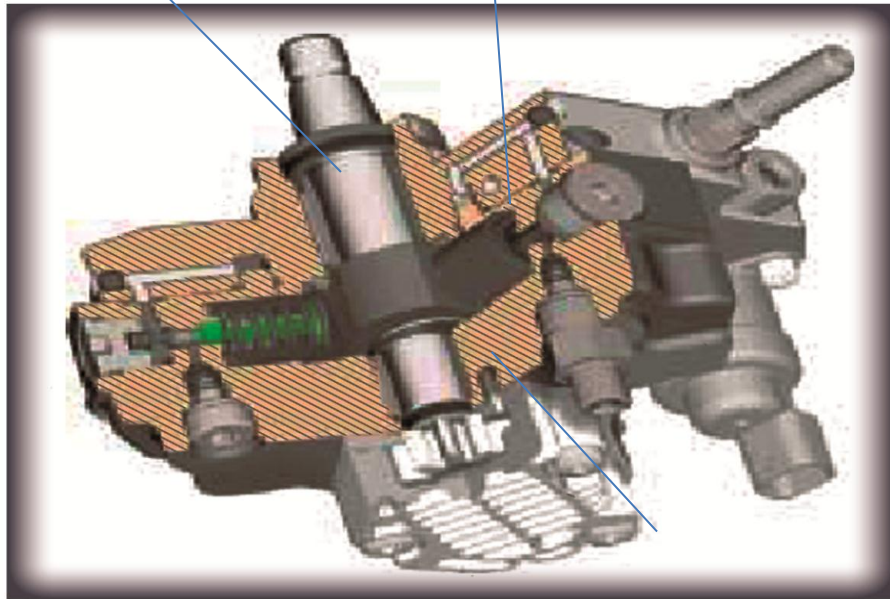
6. Bomba de alta presión con bomba de engranajes.
